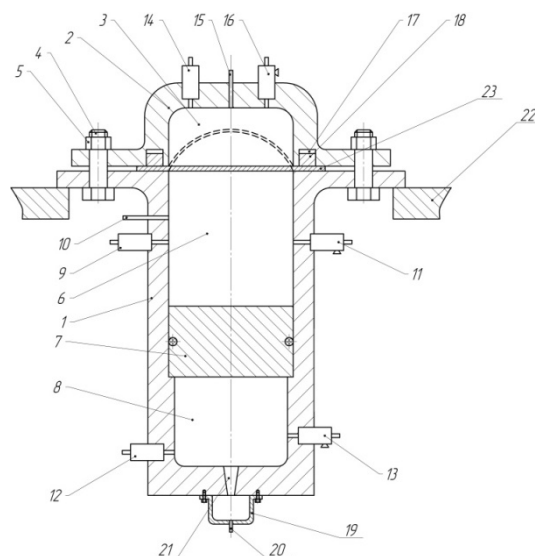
Схема устройства газовой штамповки с поршневым мультипликатором давления
